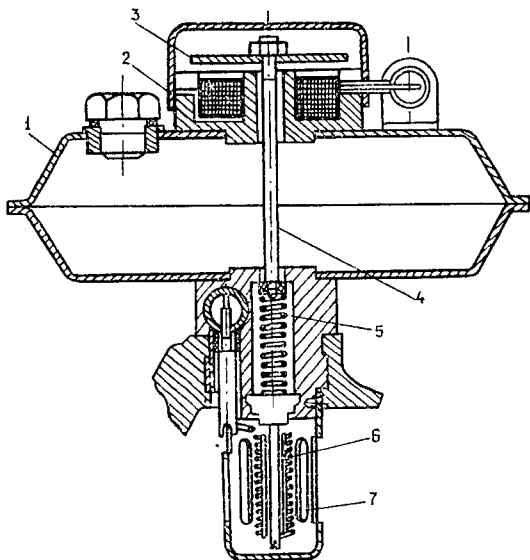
Электрофакельный подогреватель воздуха двигателя СМД:
